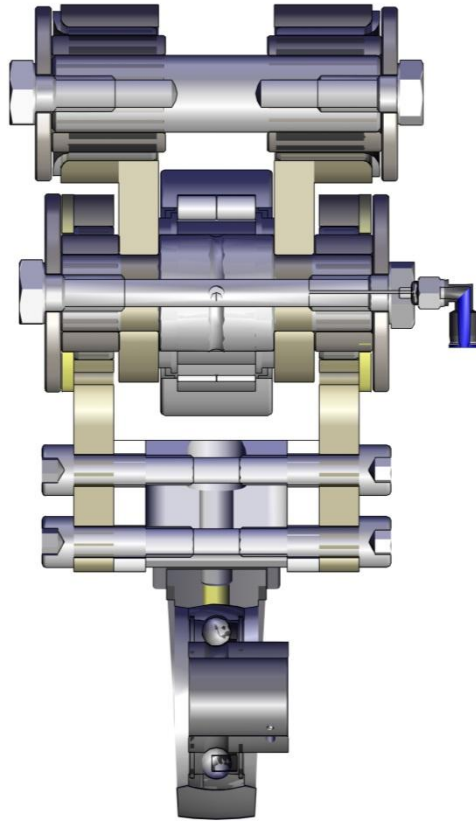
Montagezeichnung Zweigelenkschwinge
